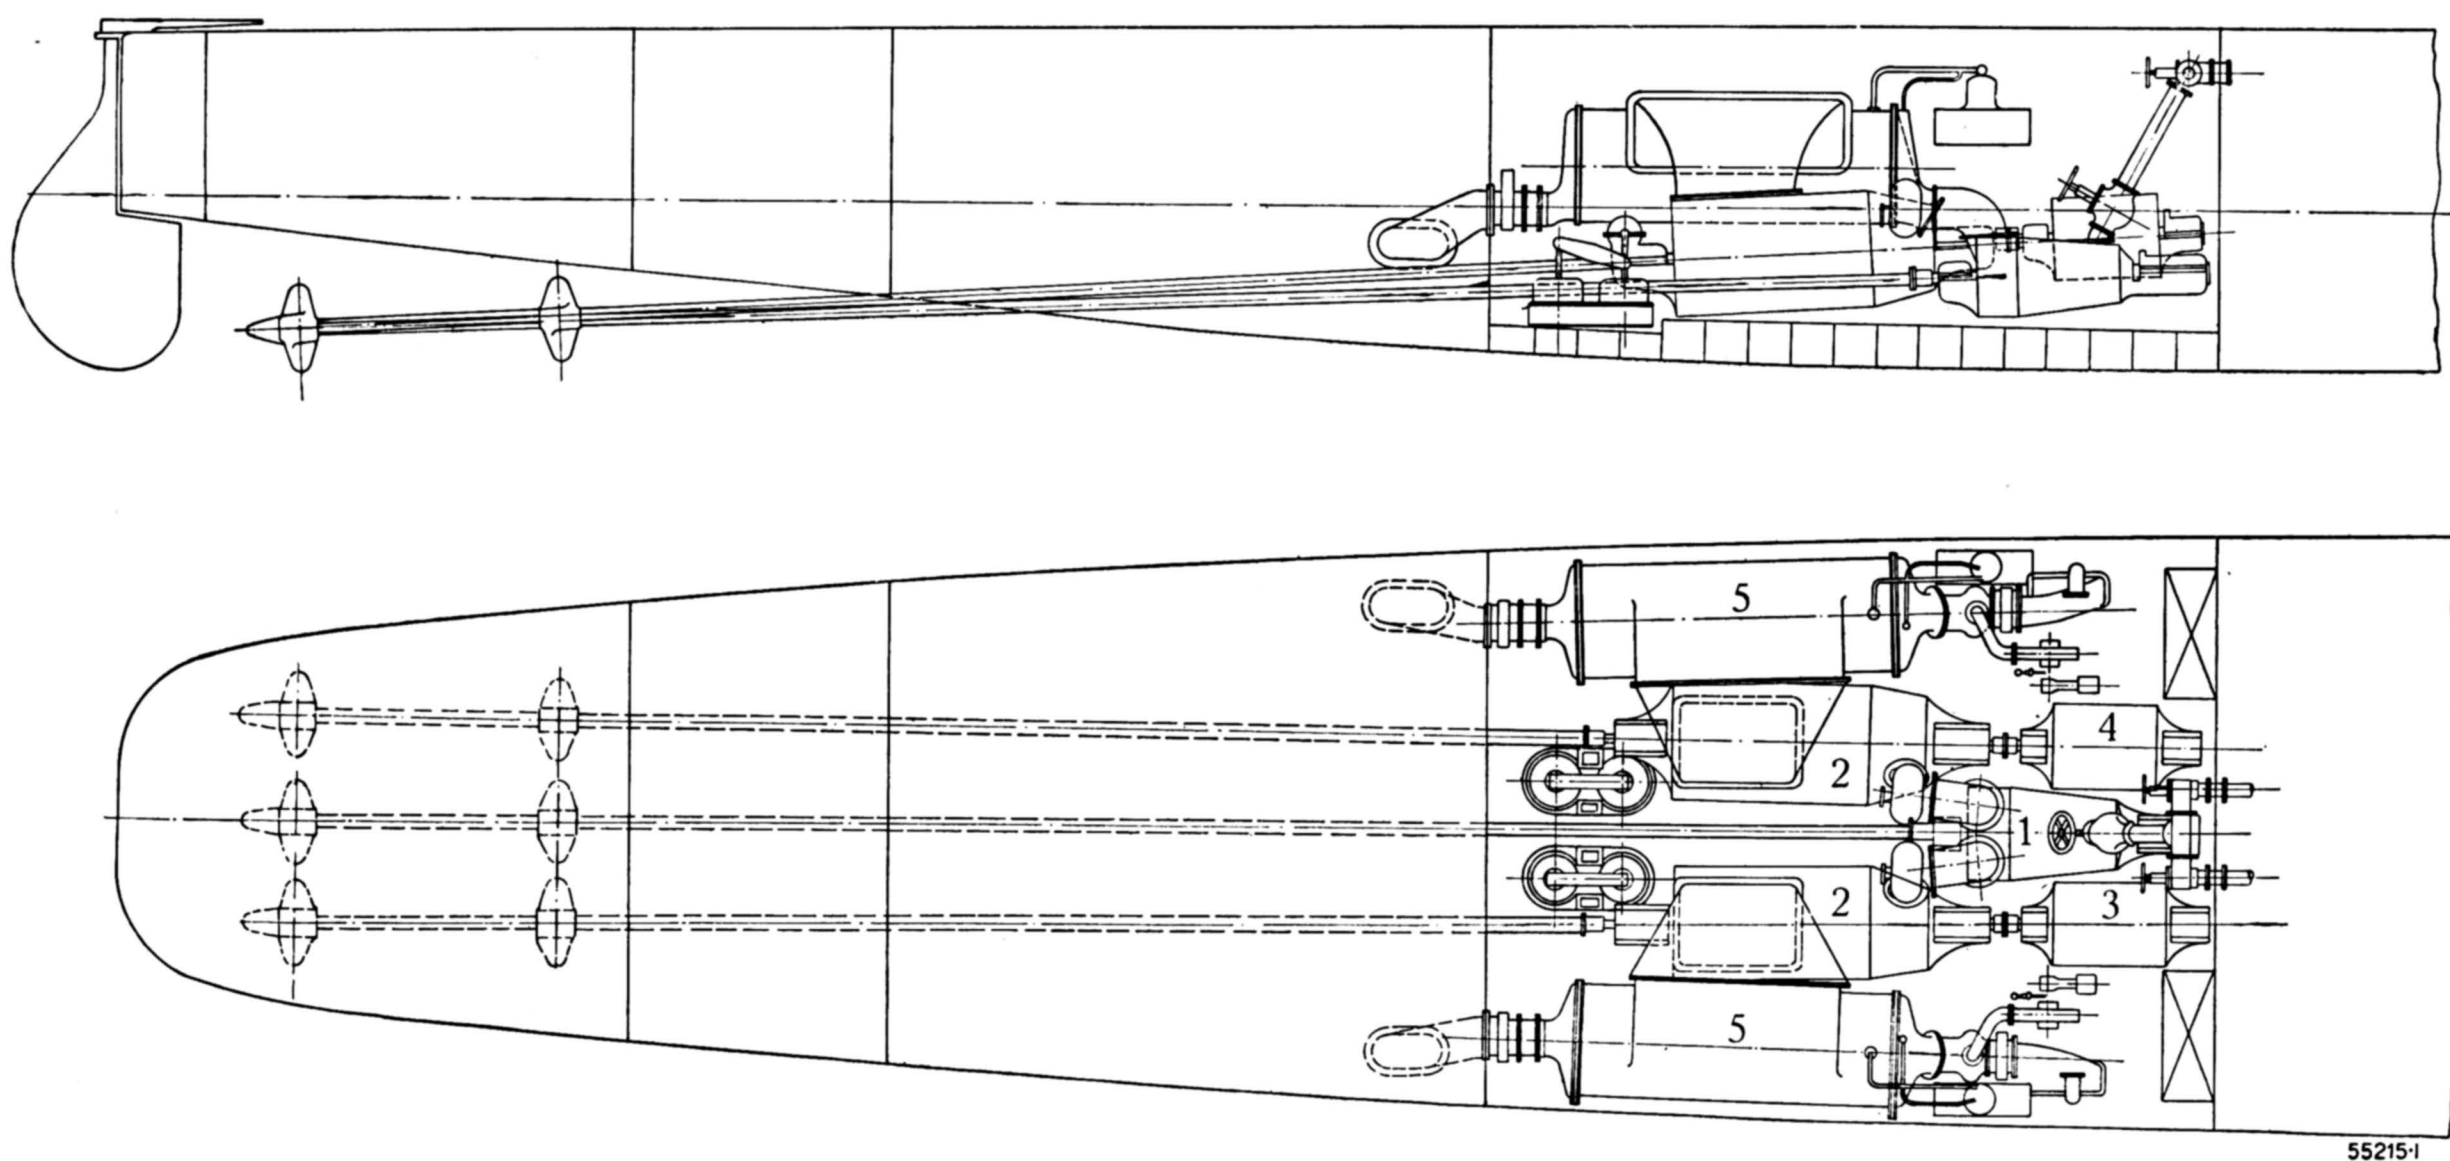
Projet définitif pour la même installation (fig. 1) avec turbine de croisière à la place des machines à pistons.
